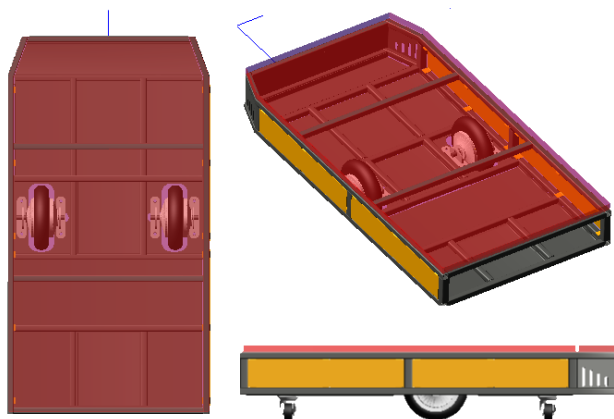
Внешний вид модели роботизированной платформы в Adams
